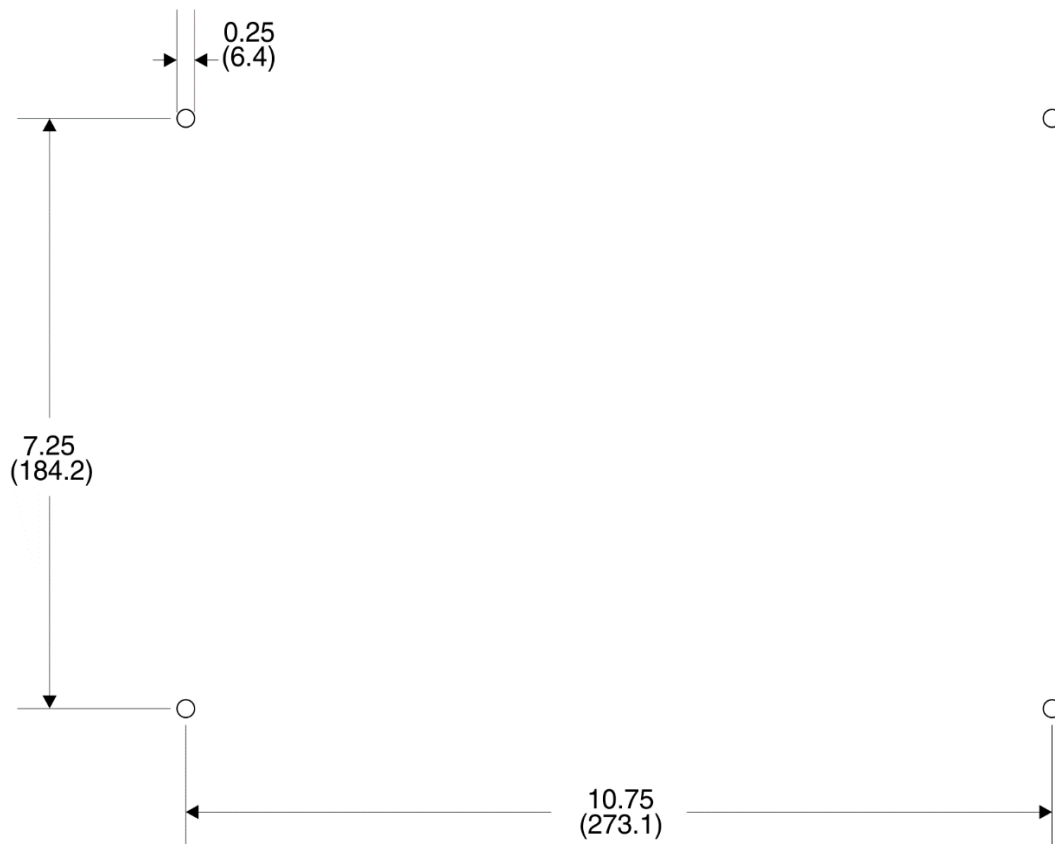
Bohrmaße für Rückwandmontage für Bauform xPxxxxxx
